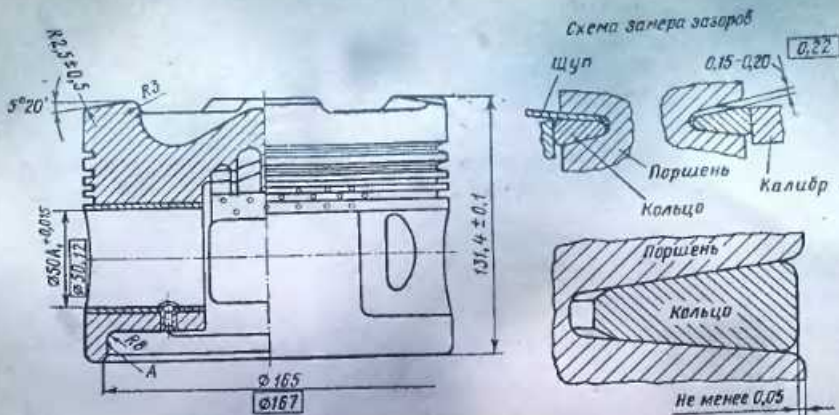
Поршень и схема замера зазоров поршневого кольца
